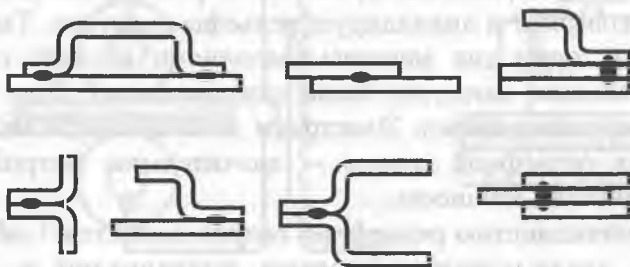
Примеры сварных соединений для точечной сварки
